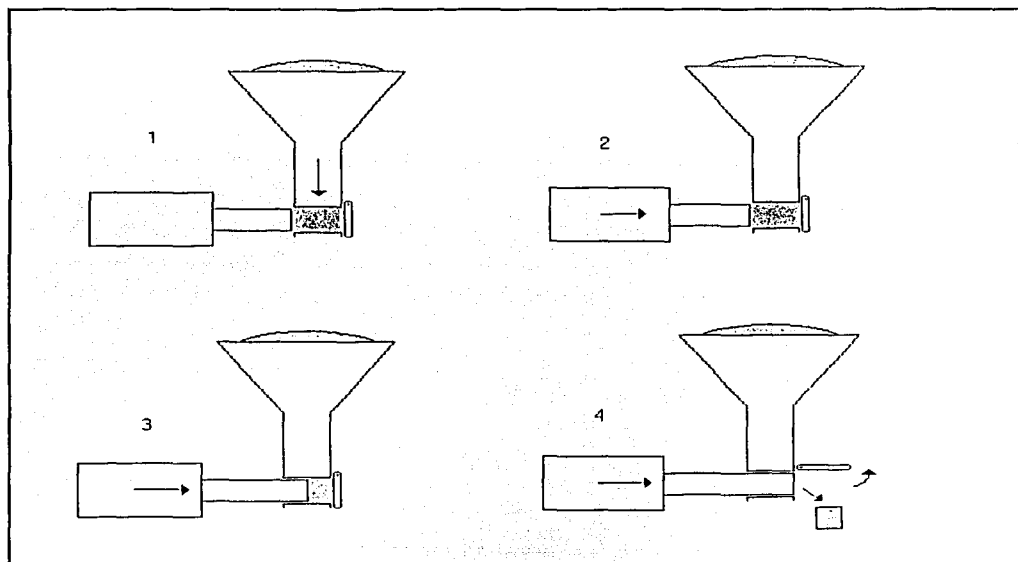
Sistema de conformado por moldeo con pistón horizontal.
